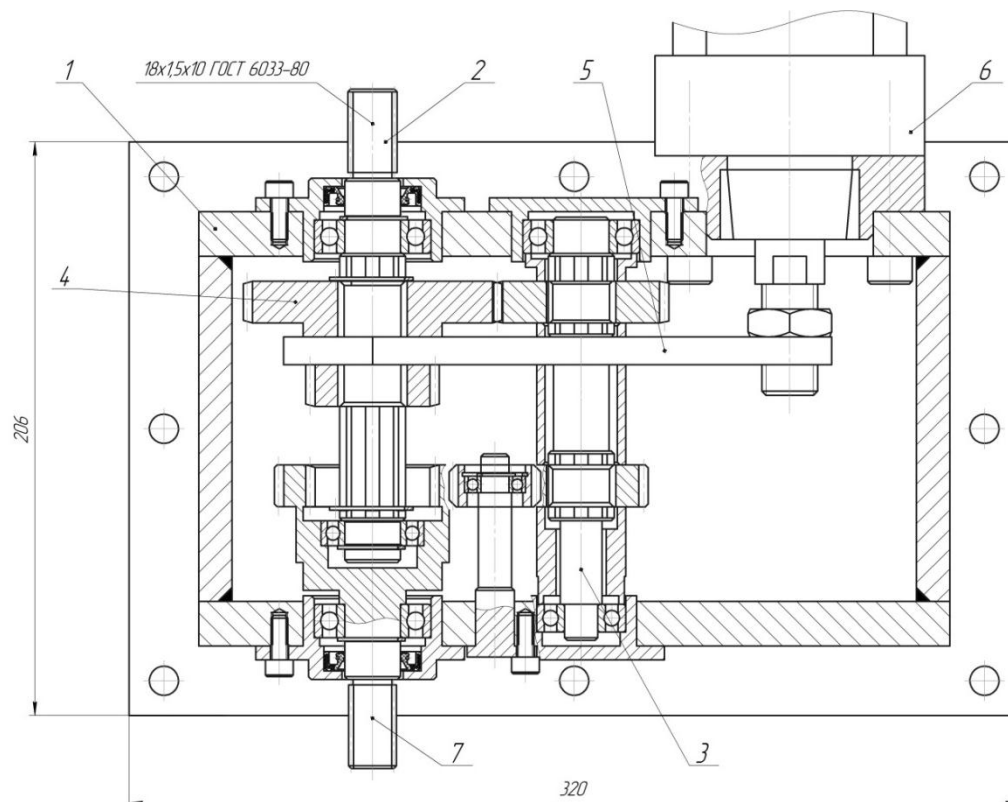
Реверс-коробка передач: 1 – корпус; 2 – входной вал; 3 – вал; 4 – блок-шестерня; 5 – вилка; 6 – пневмоцилиндр; 7 – выходной вал
